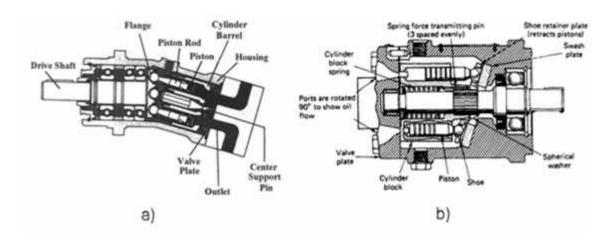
Bomba de pistones axiales (a) eje inclinado (b) plato basculante.
